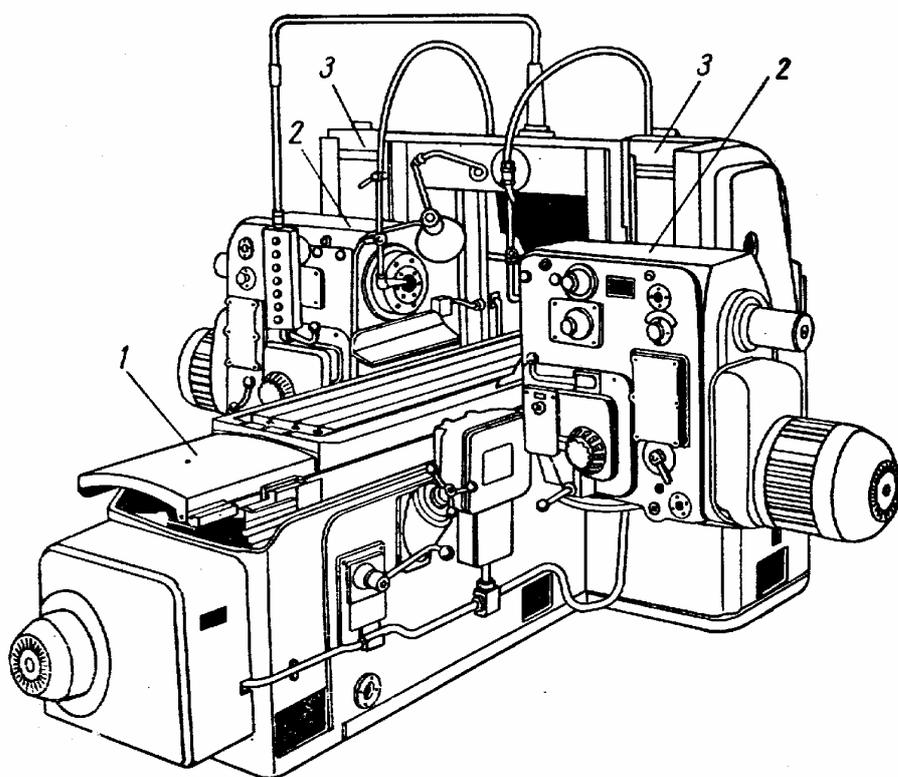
Двухстоечный продольно-фрезерный станок А662
